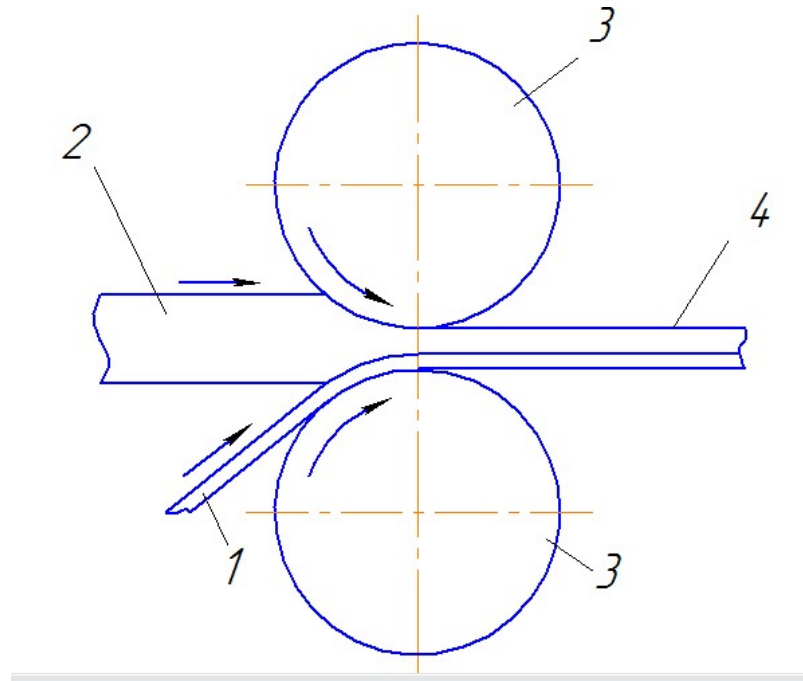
Отримання біметалів при деформації складової біметалічної композиції: 1 - тверда; 2 - м'яка; 3 – прокатні валки; 4 - біметал
